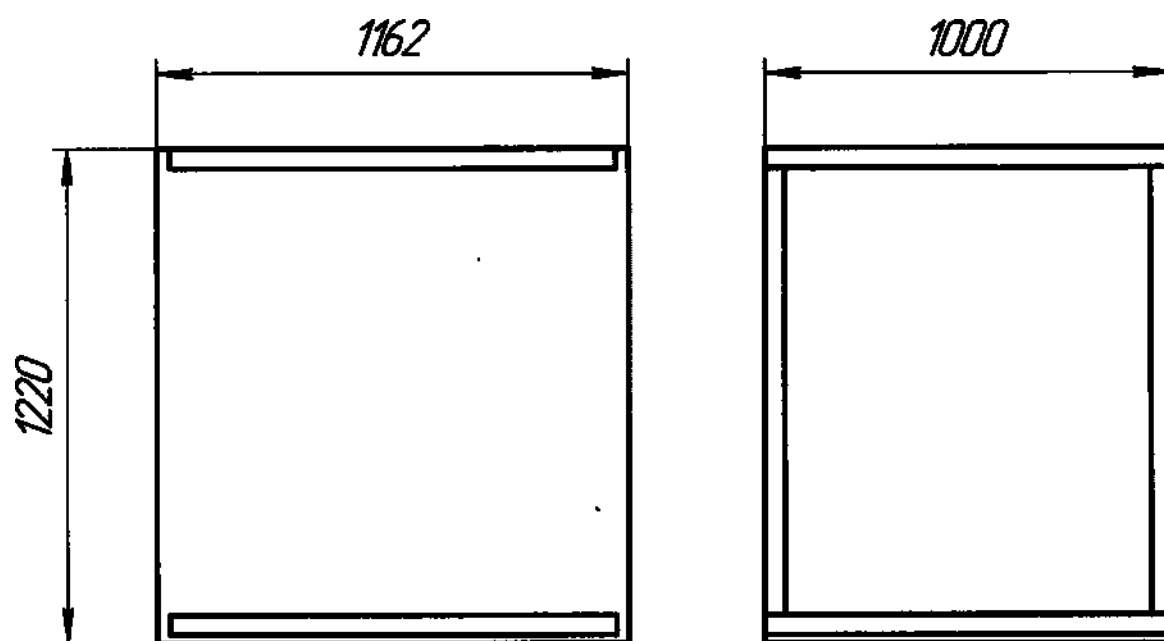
Габаритные размеры упаковочного ящика тренажера
